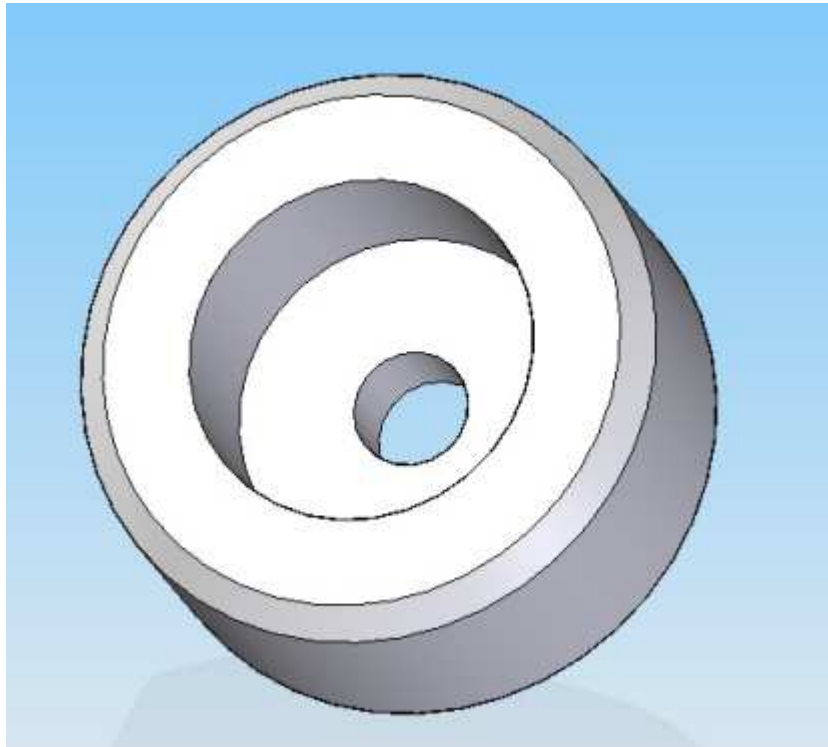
Detalle de la vista en planta de la cámara de medida
